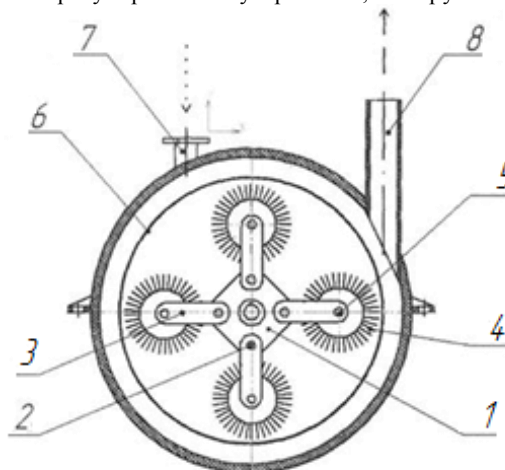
Камера тонкого помола: 1 – ступица; 2, 5 – ось; 3 – сержа; 4 – щетка; 6 – сетчатый экран; 7 – патрубок добавок; 8 – выгрузочный патрубок
